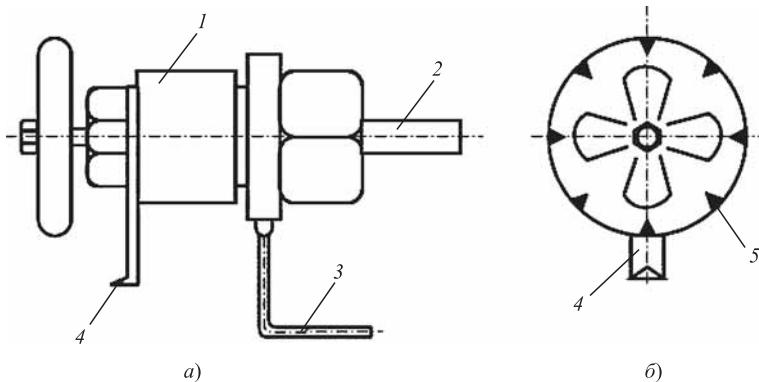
Общий вид пробоотборника (а) и схема его регулировочного устройства (б):
